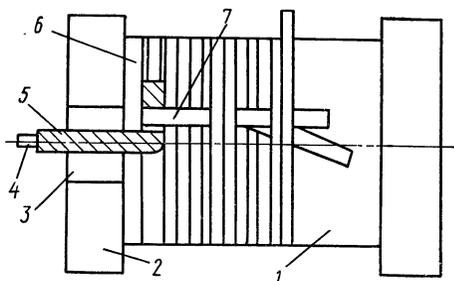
Крепление концевой изоляции и первых витков цилиндрической обмотки ВН:
